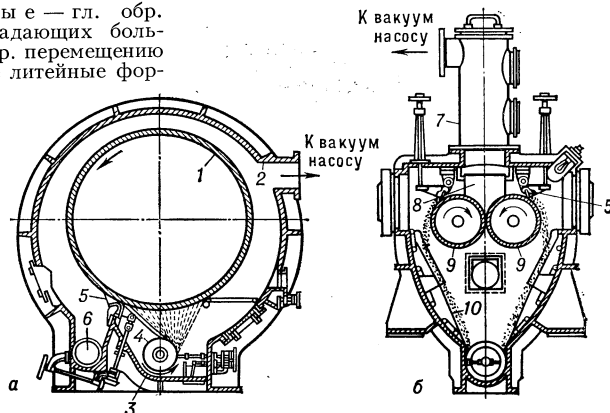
Вакуум-сушилки: а — одновальцовая; б — двухвальцовая; 1 — полый барабан (валец); 2 — корпус; 3 — корыто; 4 — распределительный валик; 5 — нож; 6 — шнек; 7 — приёмный колпак; 8 — сборник; 9 — вальцы; 10 — наклонные стенки.
